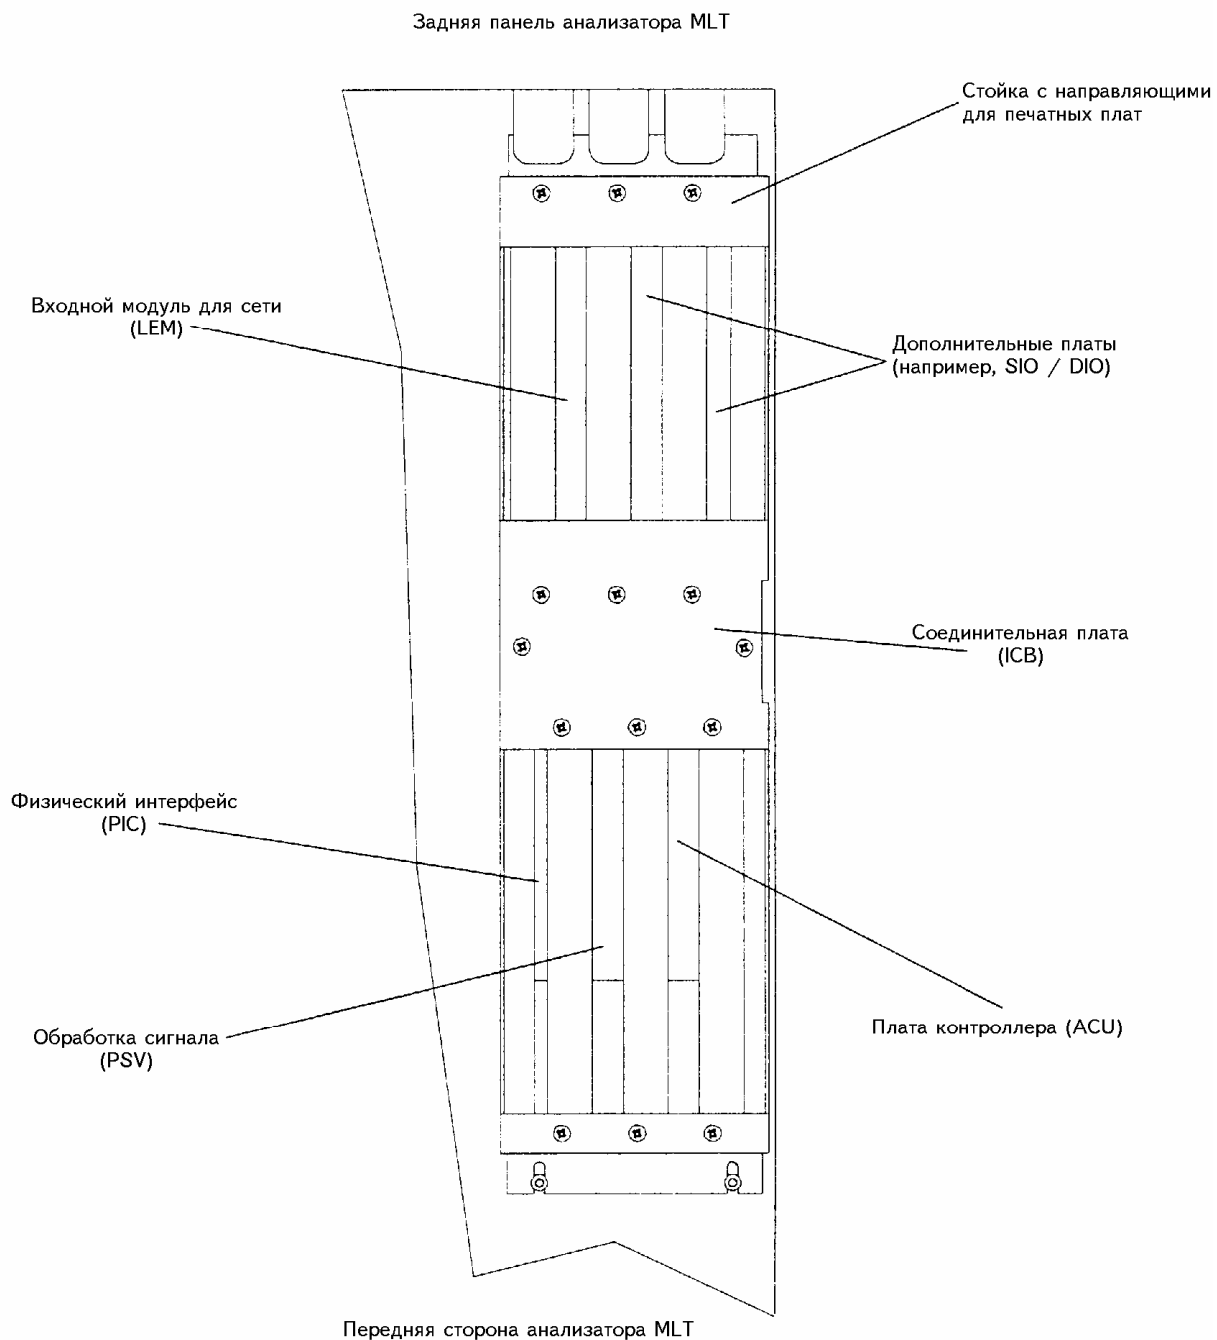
Стойка с направляющими для печатных плат для MLT 1/3/4, вид сверху
